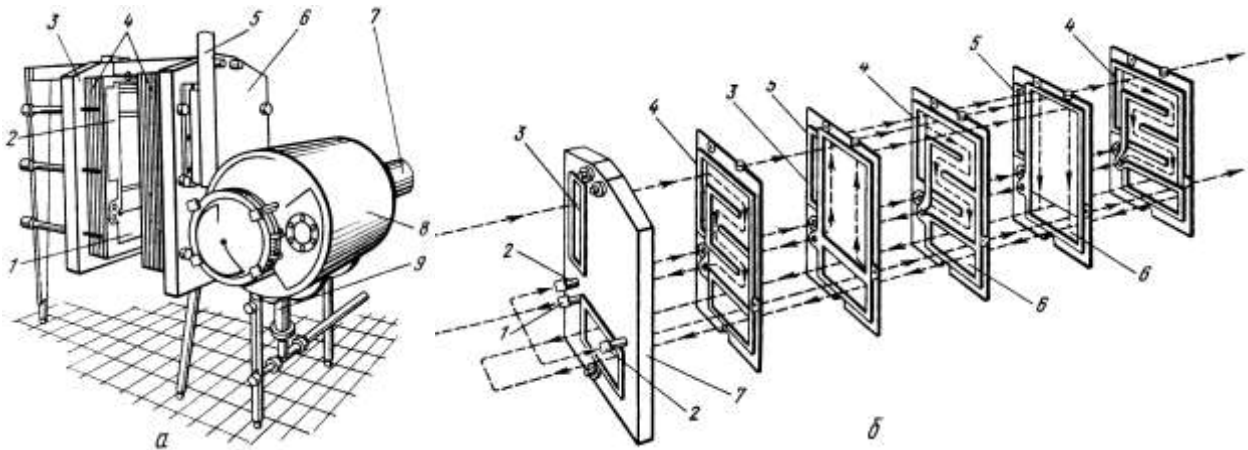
Схема однокорпусної вакуум-випарної установки із пластинковим калоризатором:
